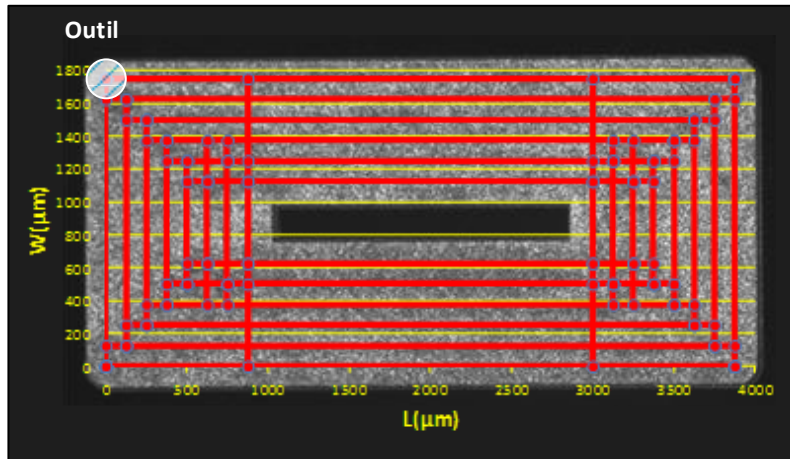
Usinage d'un insert avec $R=50\%$: parcours d'outil d'une couche en rouge superposé au résultat d'usinage (caméra 2).
